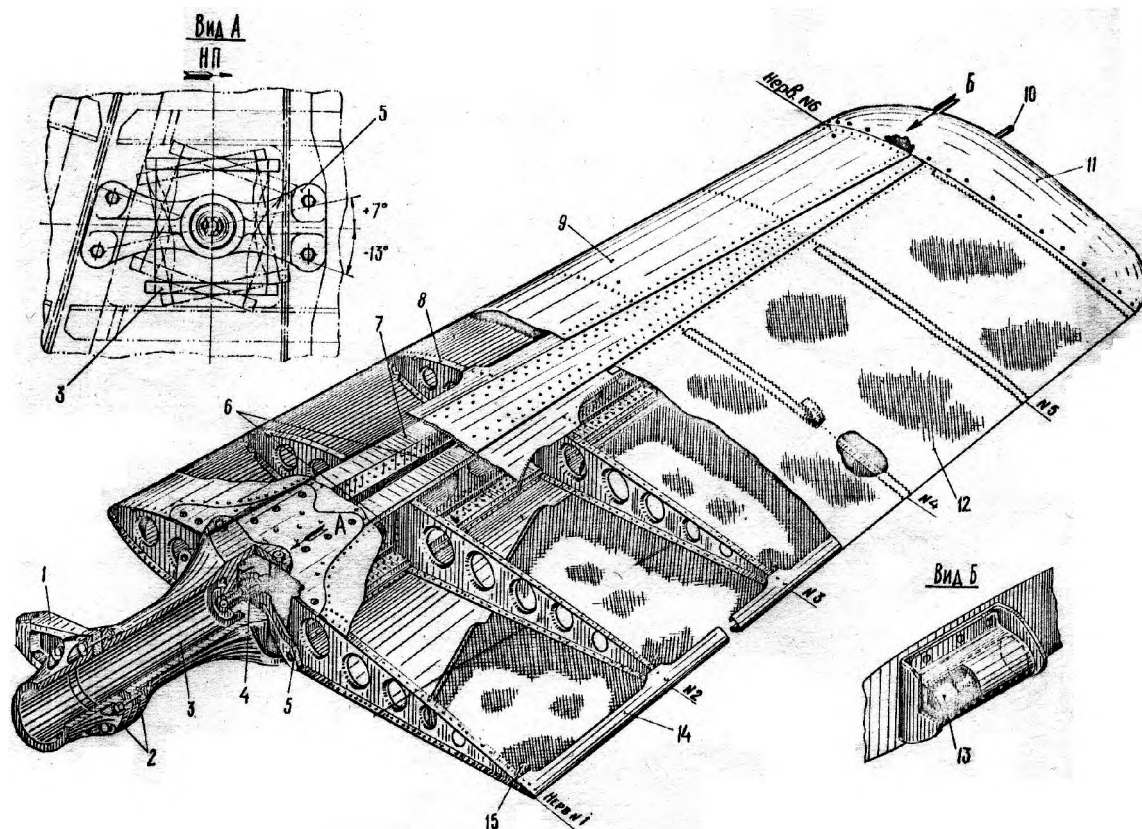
Каркас консоли стабилизатора вертолета Ми-24А [13]:
